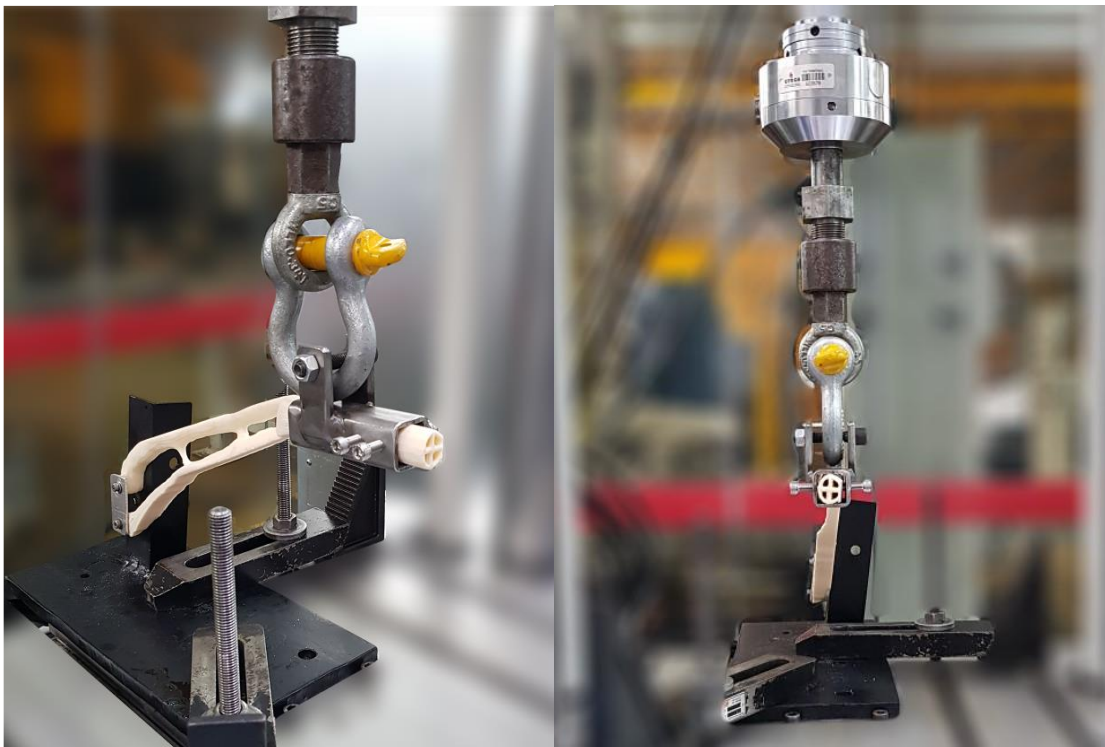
Conjunto montado pronto para realizar o ensaio. Fonte: O Autor.
